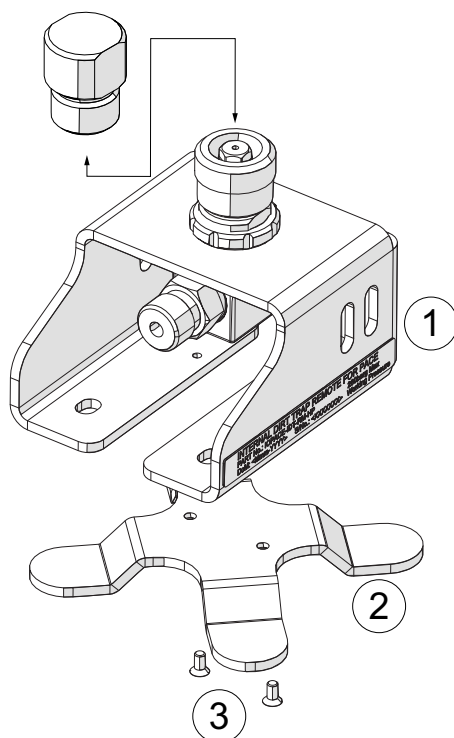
Montaggio o rimozione del supporto dalla staffa
